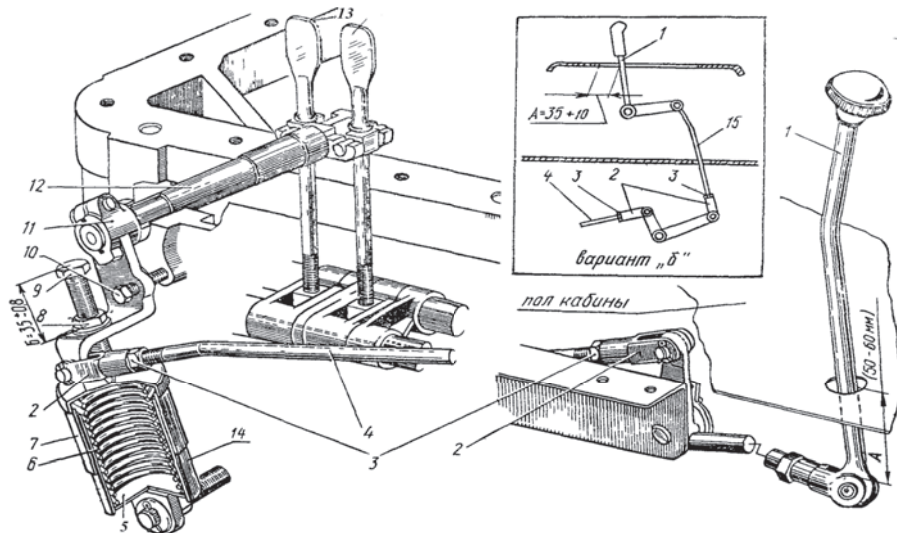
Управление задним ВОМ. 1 — рычаг управления; 2 — рег. улитровочная вилка; 3, 8 — контргайки; 4 — тяга; 5 — стакан пружины; 6 — пружины; 7 — верхний стакан; 9 — упорный болт; 10 — у становочный болт (только для рег улитровки); 11 — рычаг ва лика управления; 12 — валик управления; 13 — регулировочные винты; 14 — нижний стакан; 15 — тяга, вариант «б» — для тракторов с унифицированной кабиной.
